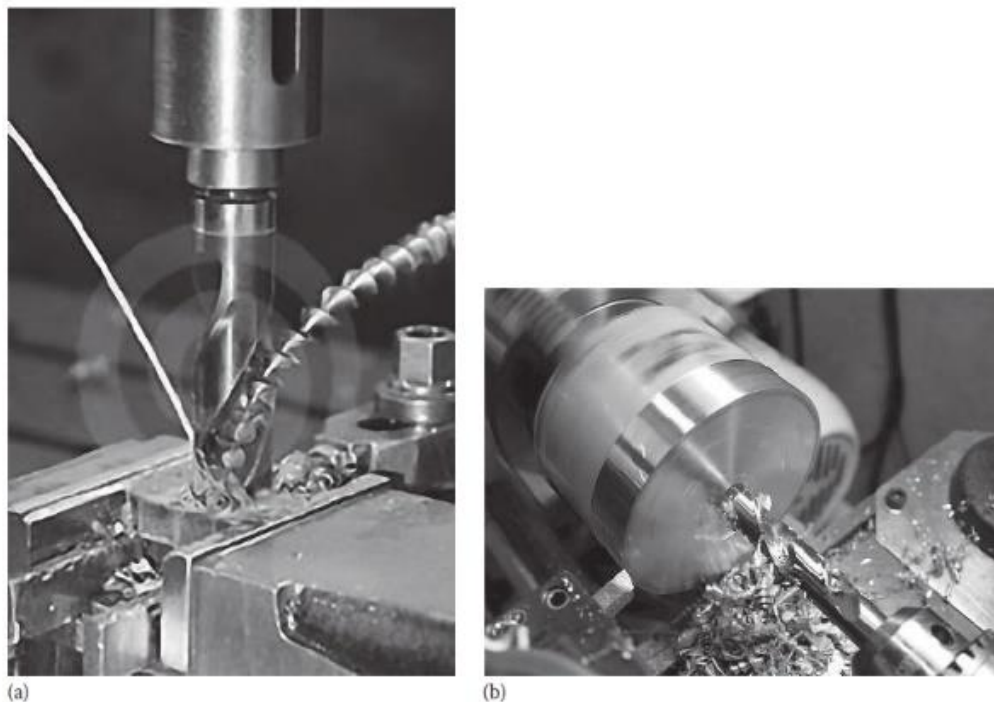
(a) Barrenado vertical (b) Barrenado horizontal [15].
